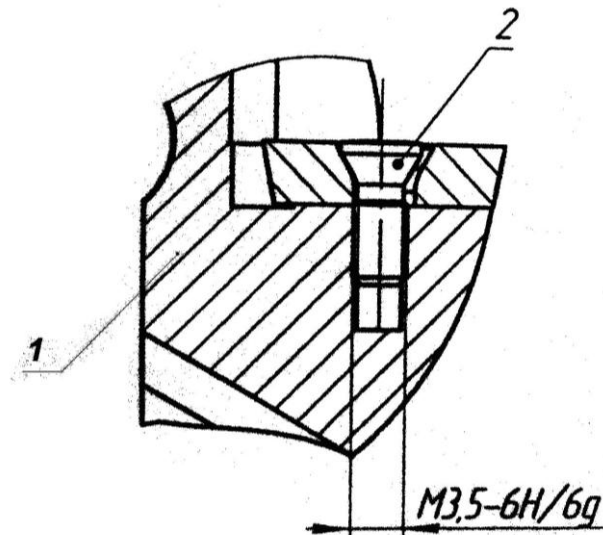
Схема кріплення пластини до корпусу фрези
